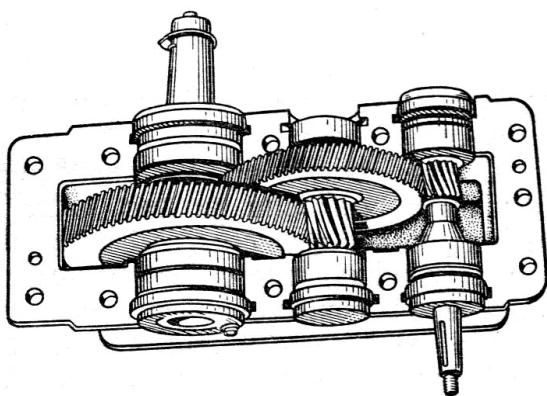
Двухступенчатый цилиндрический редуктор (Ц2), выполненный по развернутой схеме
